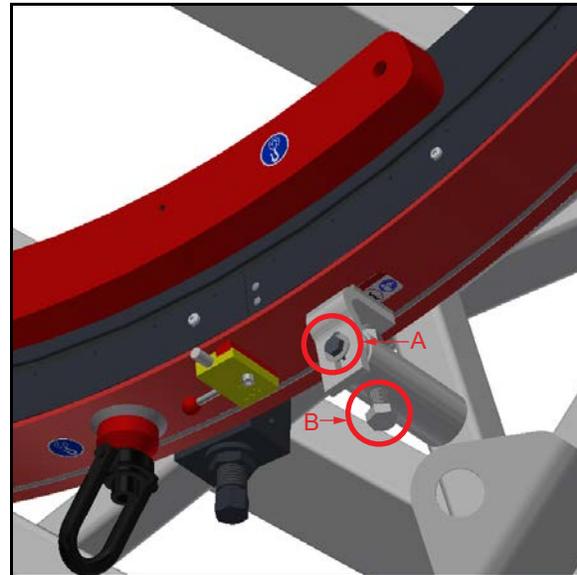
EMPLACEMENT DES VIS EXTERNES (ILLUSTRATION AVEC LA MACHINE ODF80)
